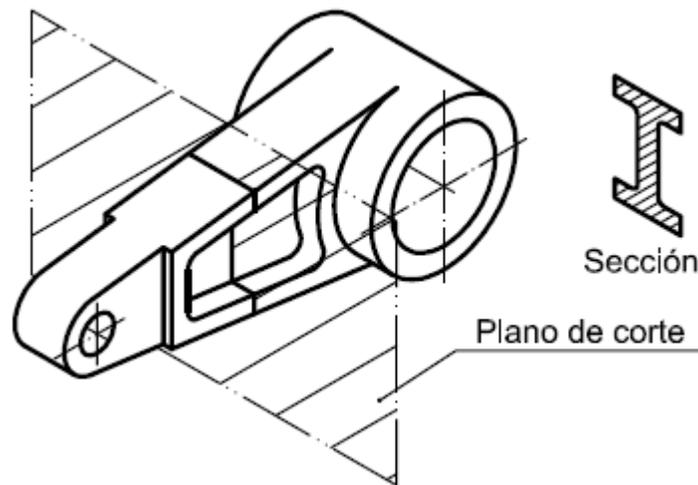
Representación espacial de la sección generada por un plano de corte.
